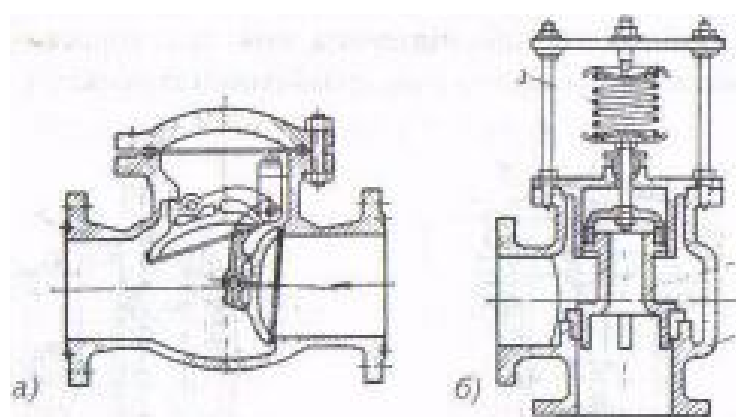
10. Клапани: а — зворотний; б — запобіжний; 1 — корпус; 2 — клапан; 3 — пружина
